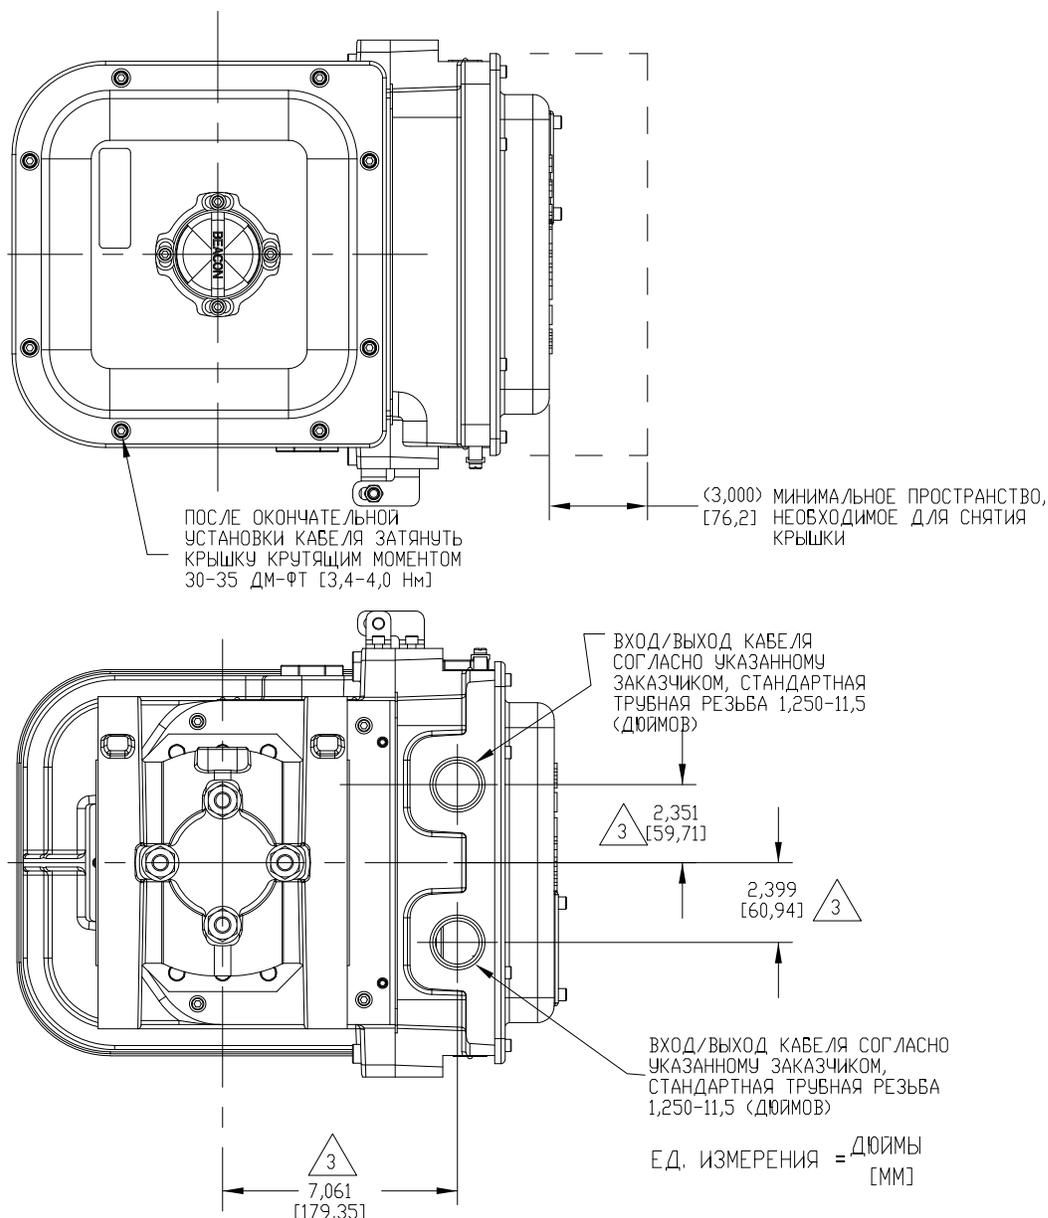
Габаритно-присоединительный чертеж RVP-200
